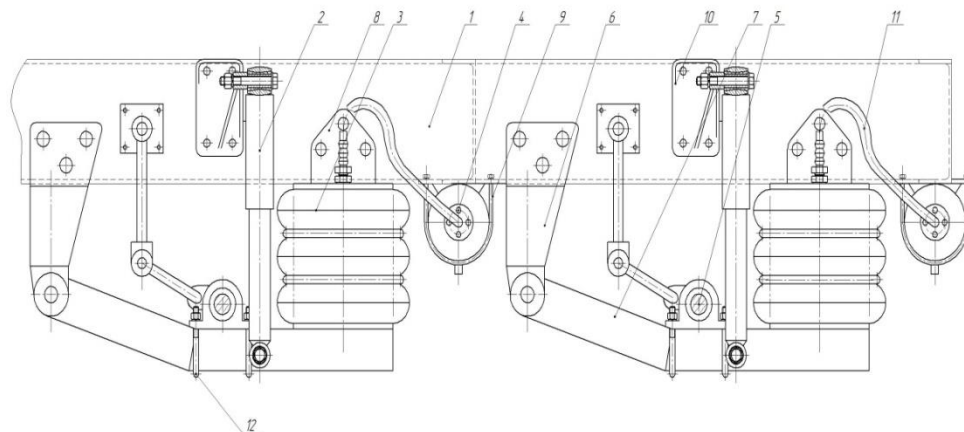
Структурная схема разрабатываемой пневматической подвески:
